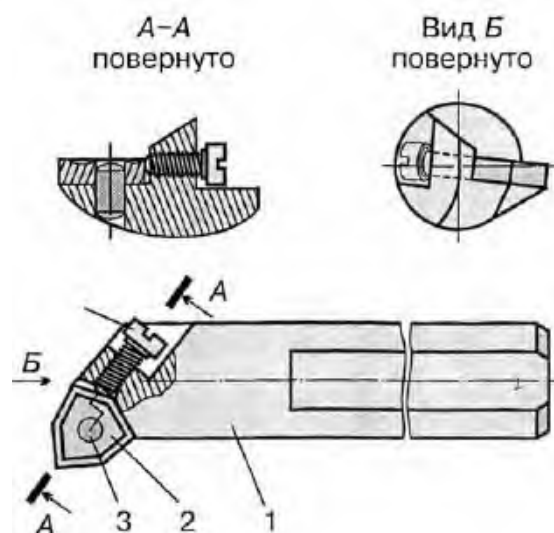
Розточувальний різець з механічним кріпленням трикромкової непереточної пластинки з твердого сплаву
